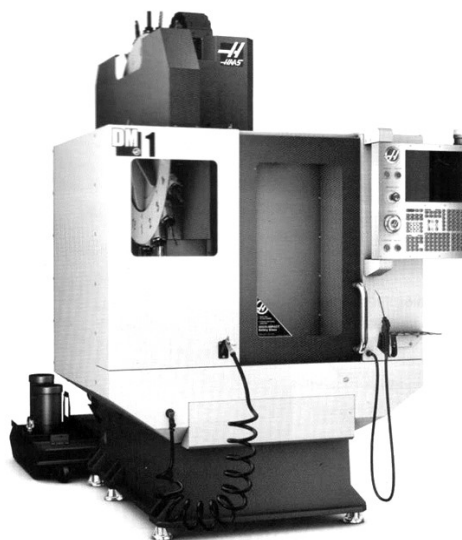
Загальний вигляд верстата з ЧПК свердлильно-різбонарізного центру DT-1
